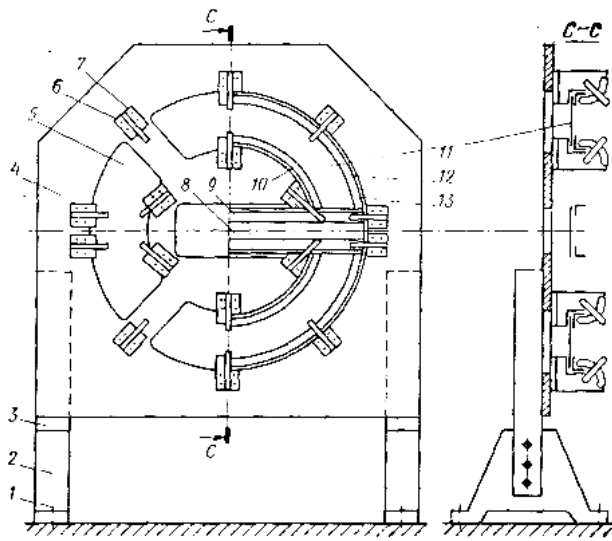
Упрощенное сборно-разборное приспособление для сборки шпангоута
